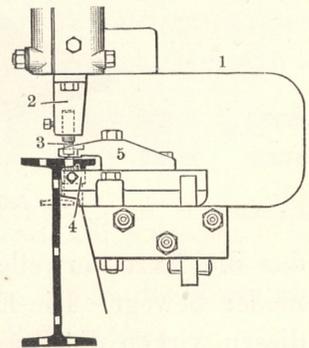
Universalwerkzeuge zur Lochmaschine.
